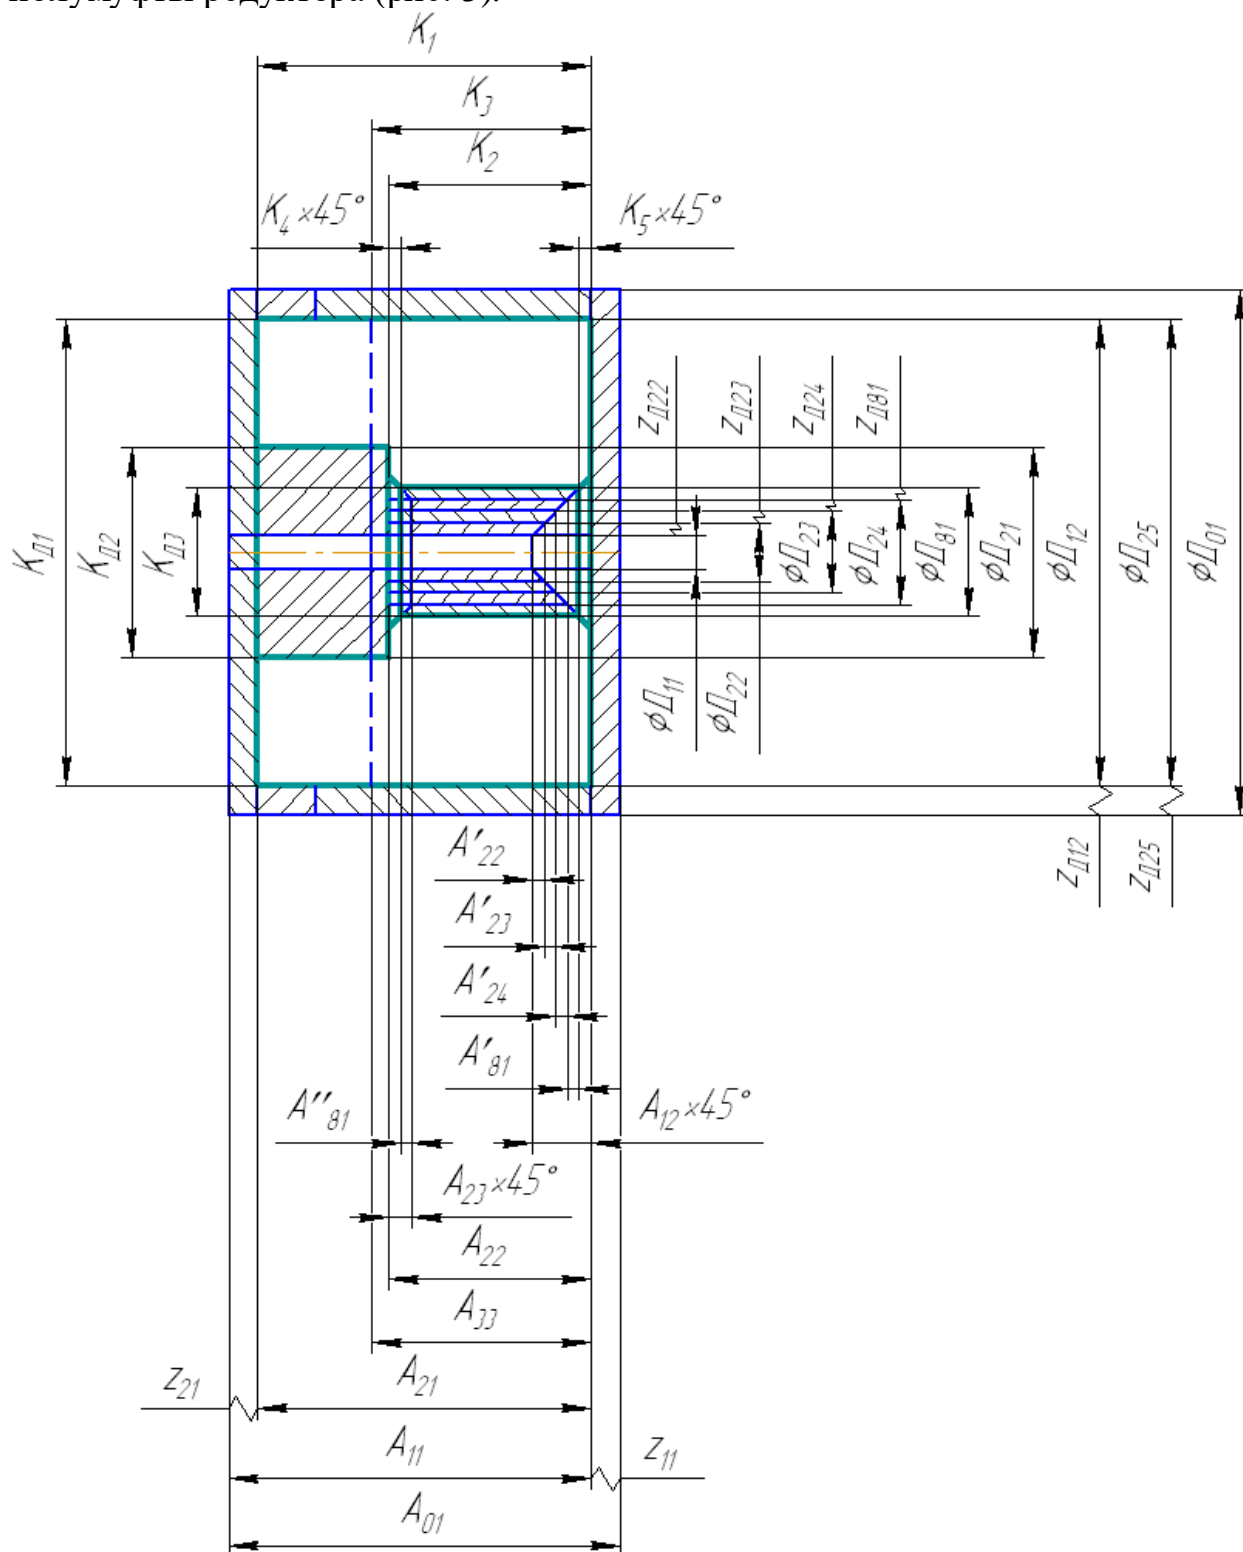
Размерная схема технологического процесса изготовления полумуфты редуктора.
